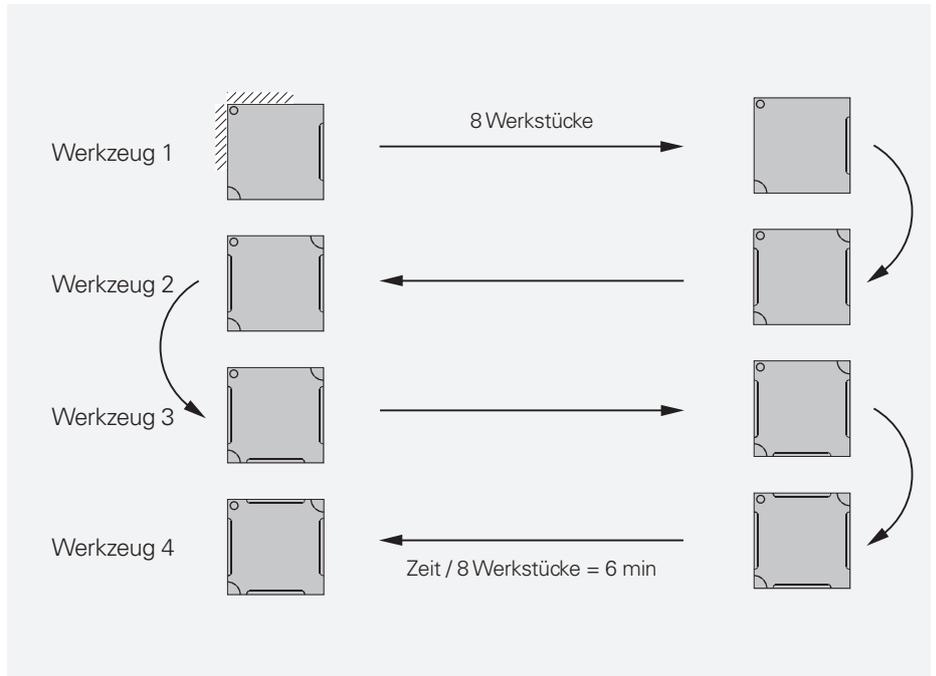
Versuchsanordnung zur Serienfertigung mit Mehrfachaufspannung. Mit insgesamt 4 Werkzeugen wurden 4 Taschen und 2 Radien jeweils 1 mm tief gefräst. Zum Nachweis der thermischen Drift infolge der Erwärmung der Kugelgewindespindel wurden die Werkstücke nach der Bearbeitung nicht ausgetauscht, sondern lediglich die Tiefenzustellung erhöht.
